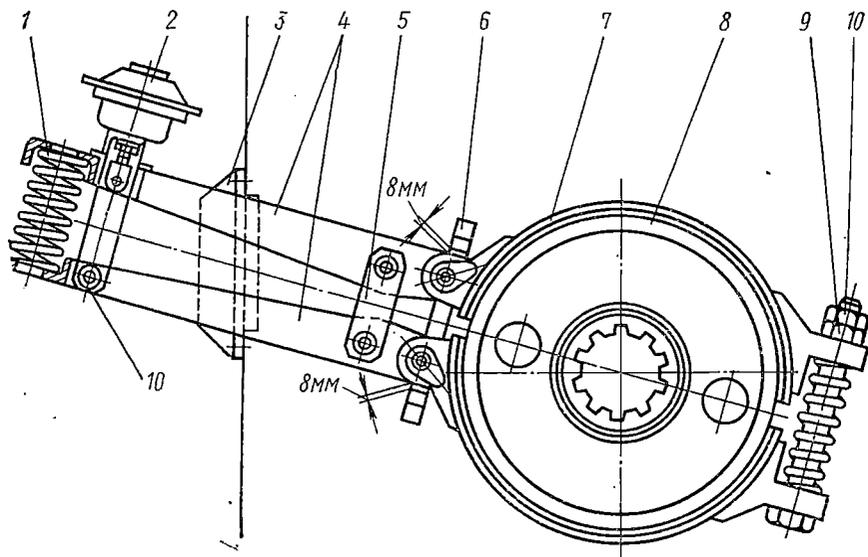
Тормоз механизма поворота экскаватора Э-652Б:
